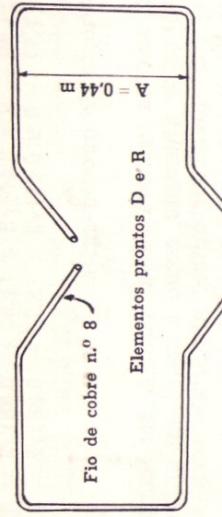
Depois de convenientemente preparado cada par de elementos ficará com o aspecto indicado nesta figura.
